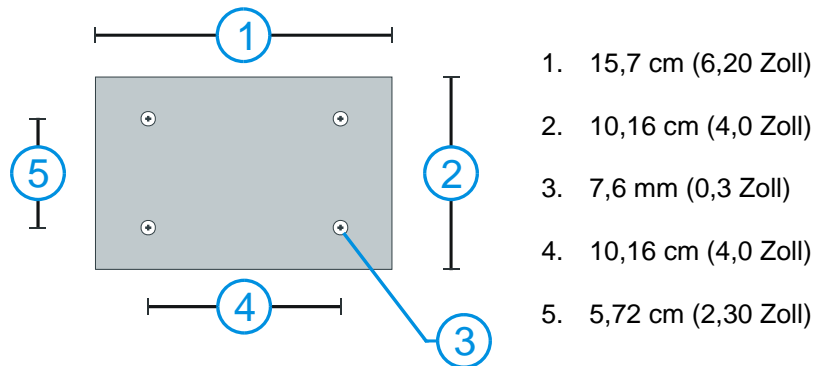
Externe VMT-Tastatur - Montageabmessungen
